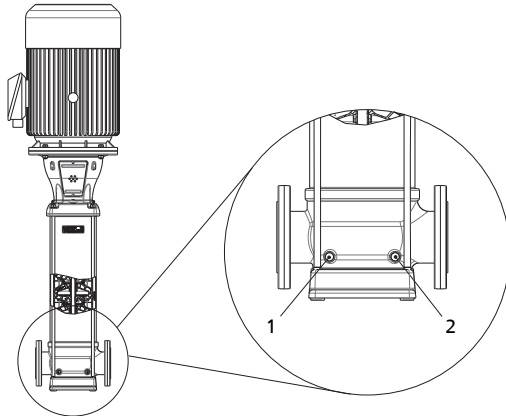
Anschlüsse zum Entleeren der Pumpe
